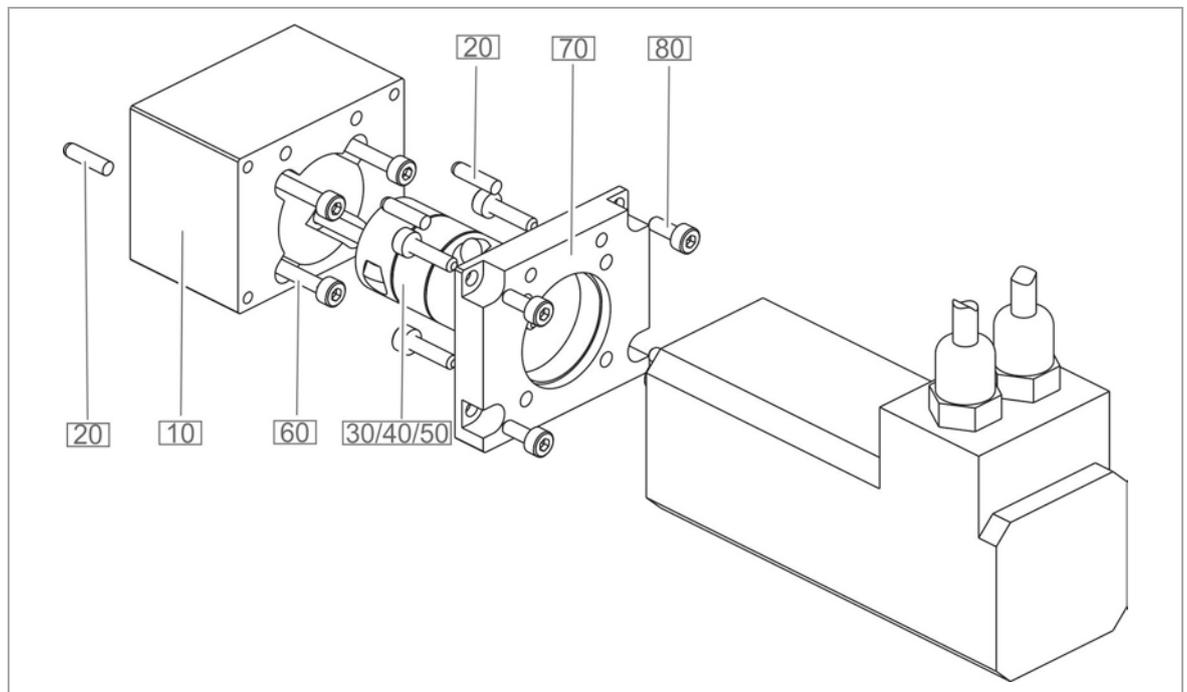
Flansch für axialen Motoranbau Lochkreis 40, Explosionsdarstellung
